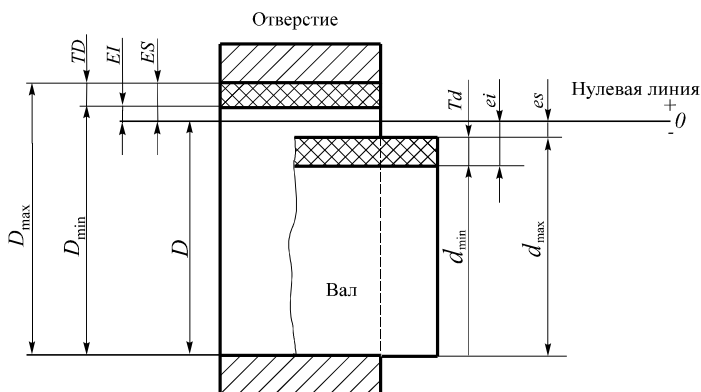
Поля допусков отверстия и вала
